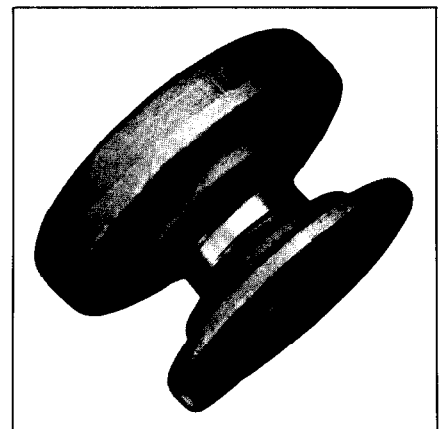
Abbrennstumpfschweißen: Kuppelungsstück für Baugeräte-Schwingantrieb (Stückmasse 15,4 kg, größter Durchmesser 217 mm) aus C 45 N, Schweißquerschnitt 3570 mm²
